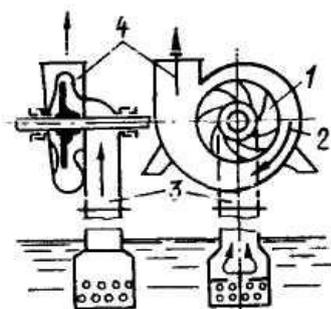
Центробежный насос: 1 – рабочее колесо (крыльчатка); 2 – корпус; 3 – всасывающий патрубок; 4 – нагнетательный патрубок;
